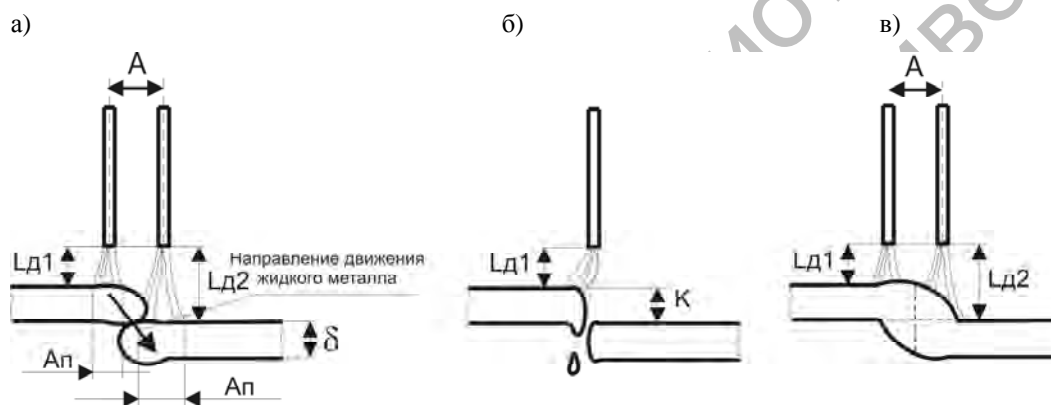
Схема, отражающая условия горения дуги при сварке соединений со смещением кромок: L_d – длина дуги; A_n – анодное пятно; A – размах колебаний
